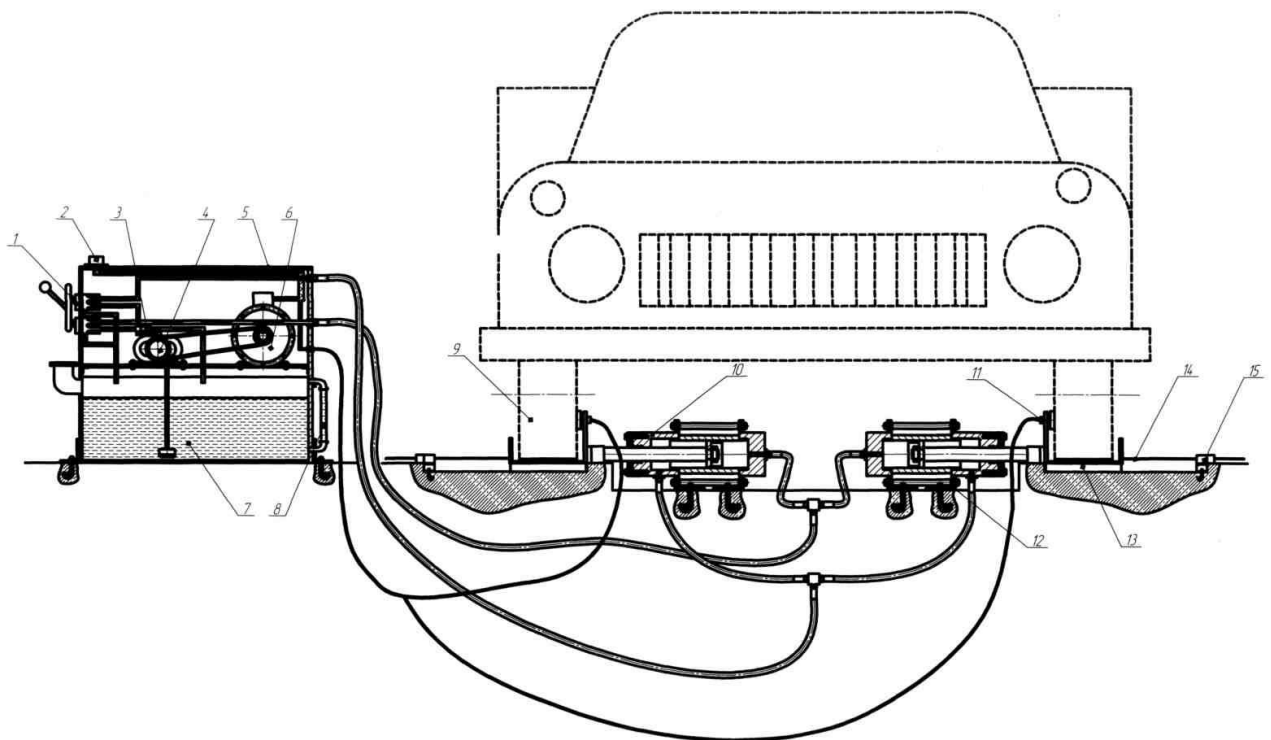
Стенд для перевірки шворневого з'єднання
